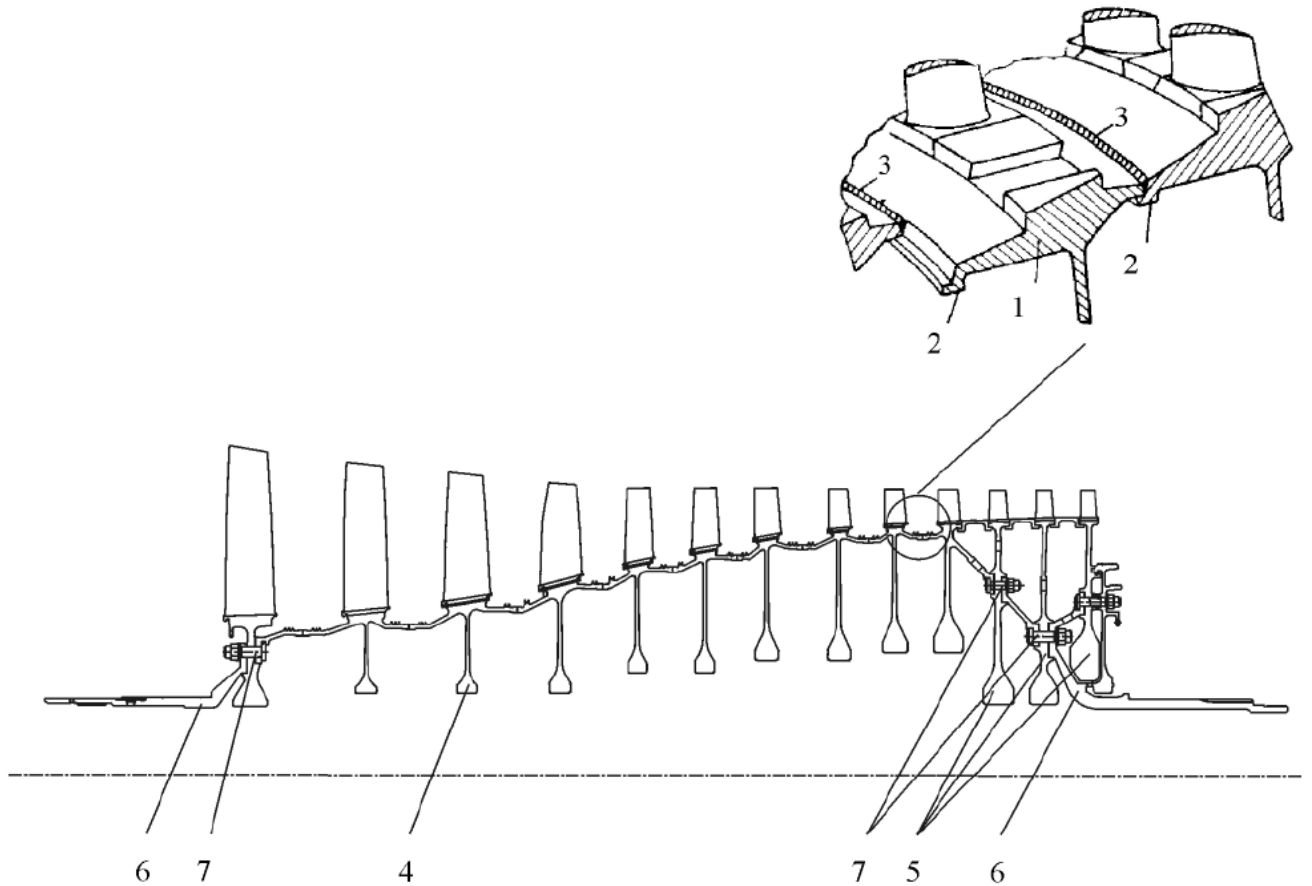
Ротор барабанно-дискового типу зі зварної титанової секцією
